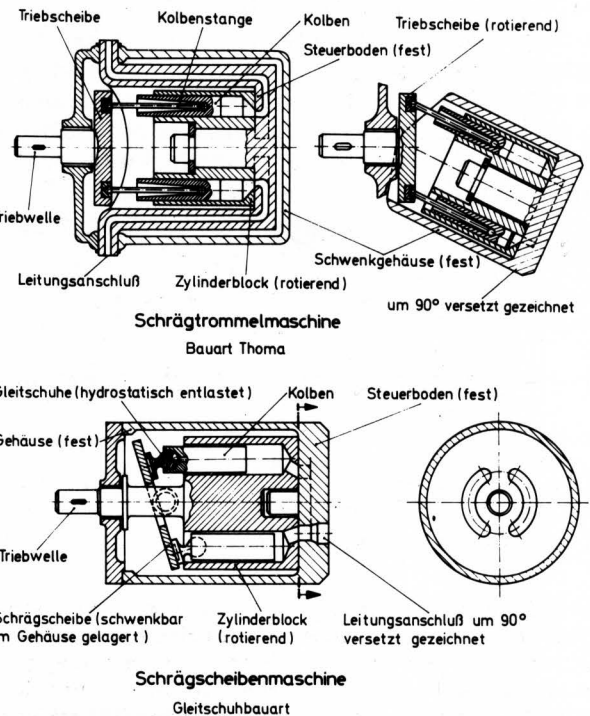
Axialkolbenmaschinen für landwirtschaftliche Schlepper (schematisch).
